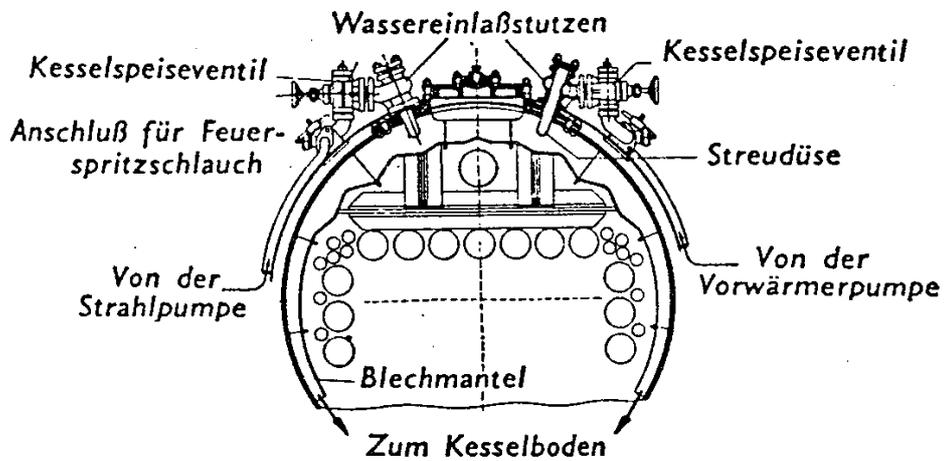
Speisewasserreinigungsanlage mit Streudüsen
